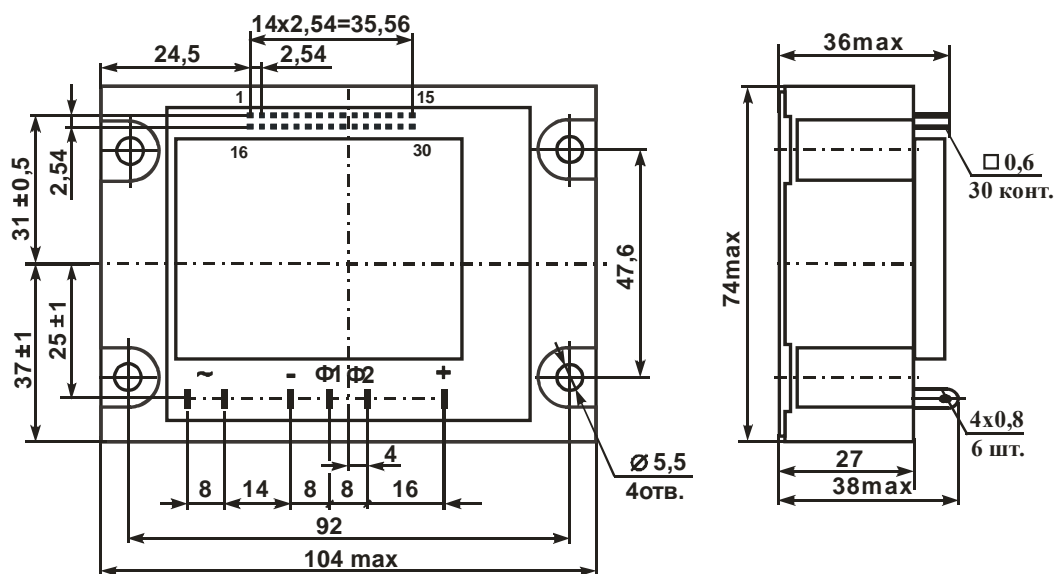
Габаритные размеры МУКДМ-5,10-1,2,6 тип силовой сборки «3»
